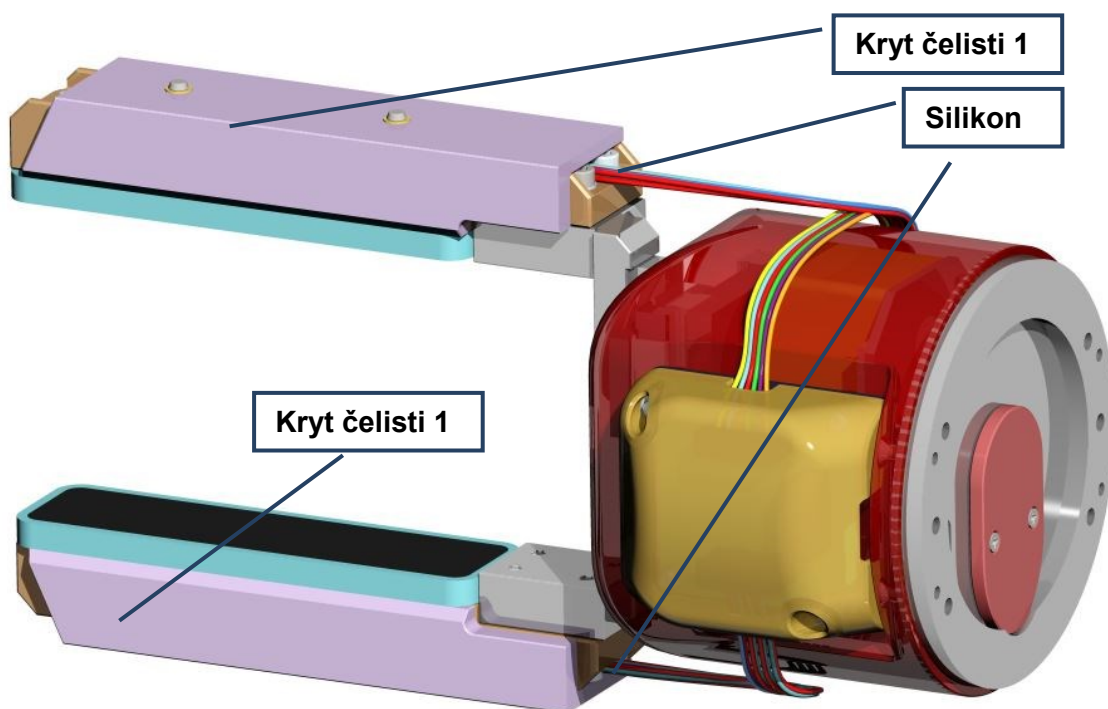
Přišroubovaná deska se zesilovačem
